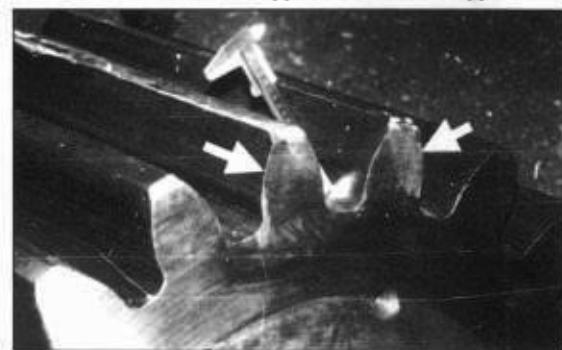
Внешний вид наплавленных зубьев с применением ЭШН после их механической обработки на зубоффрезерном станке
